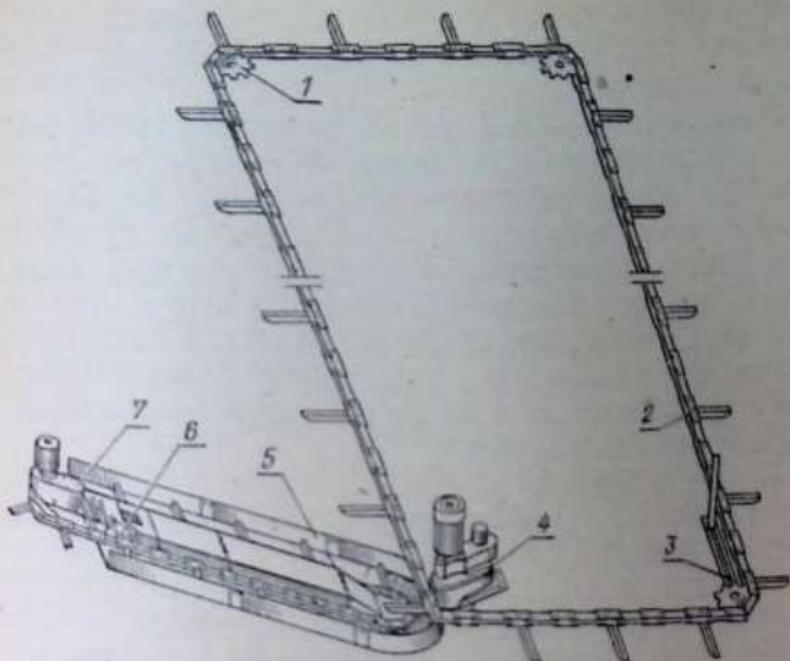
Устройство транспортера скребкового для уборки навоза ТЧН-3.0Б:
